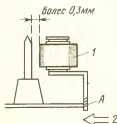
Регулировка зазора между тономаном и прижимным роликом: 1 — прижимной ролик; 2 — направление изгиба уголка для увеличения зазора
